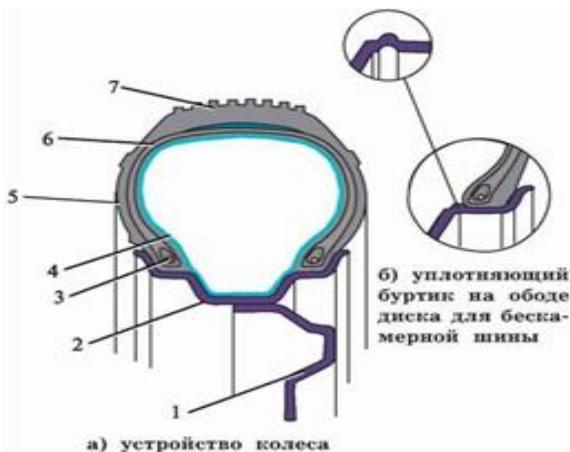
Колесо легкового автомобиля: 1 – диск колеса; 2 – обод; 3 – борт; 4 – камера; 5 – боковина; 6 – корд; 7 – протектор
